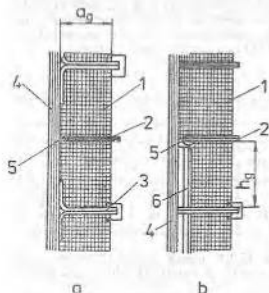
Înfășurarea secționată (în galeți) depănată direct pe cilindru izolant: a — cu galeți de aceeași dimensiune radială (grosime); b — cu galeți de dimensiuni radiale diferite; 1 — galeț; 2 — disc izolant; 3 — disc izolant răsfrînt; 4 — cilindru izolant; 5 — legătură interioară; 6 — suport de compensare.
